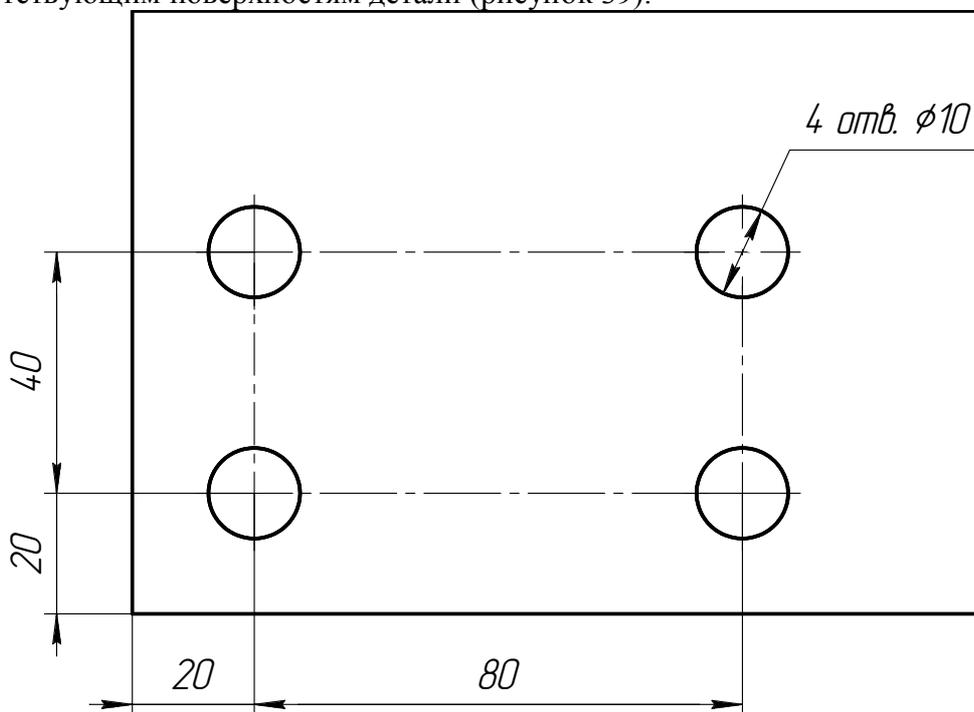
Нанесение размеров на расположение одинаковых отверстий на несимметричной детали
